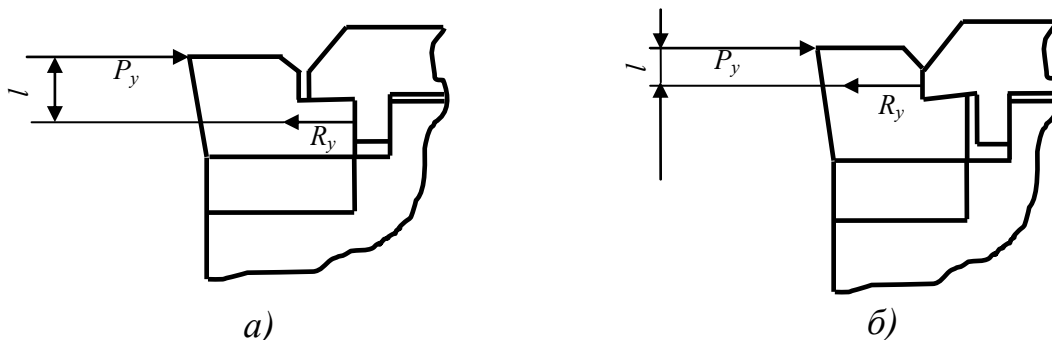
Схеми базування різальної пластини у вузлі кріплення збірного прорізного токарного різця для важкого різання: а) базування з «нижнім» упором; б) базування з «верхнім» упором
